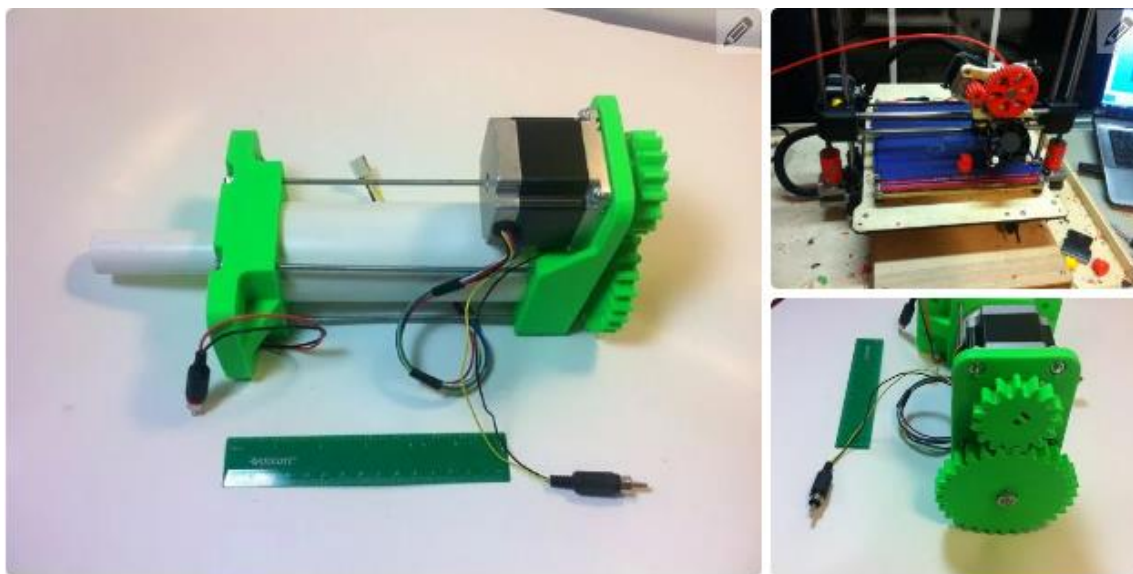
Aplicaciones de engranajes rectos por FDM, Fuente: [21].
